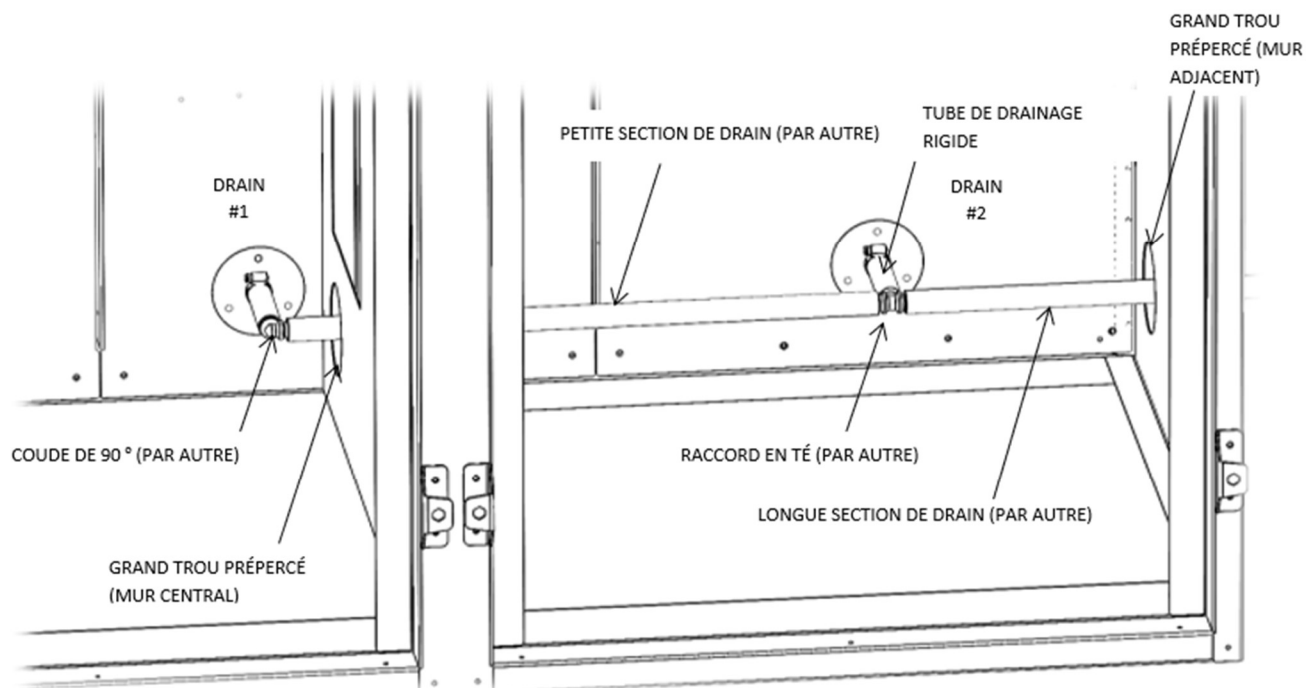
ASSEMBLAGE DE DRAINAGE TYPIQUE
